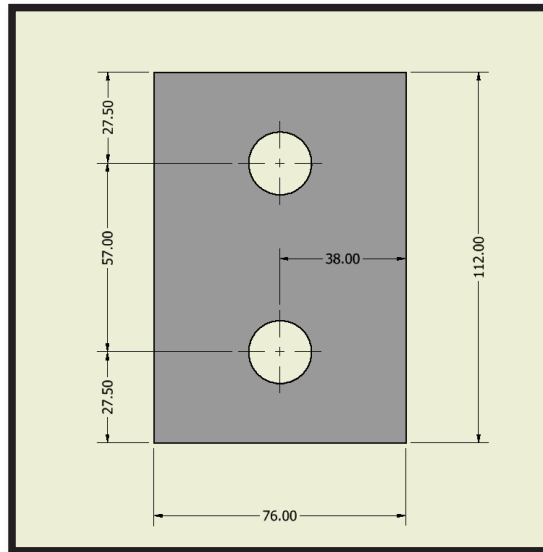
Dimensiones de la placa para conexión viga de carga-columna posterior.
